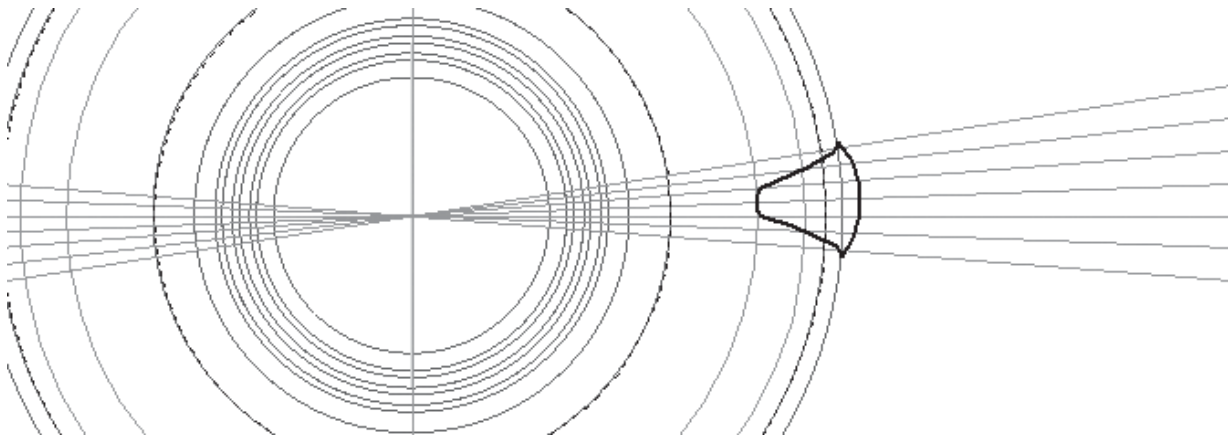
Ескіз вирізу між зубами шестерні
